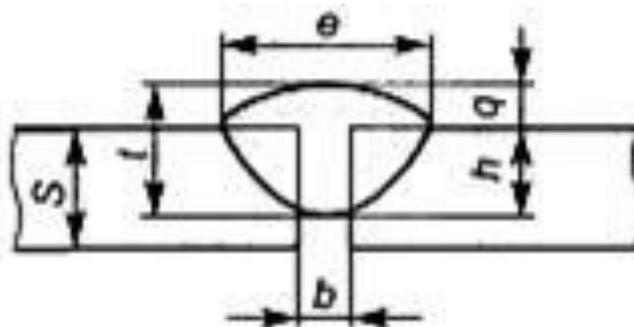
Основные геометрические параметры шва: S – толщина свариваемого металла; e – ширина сварного шва; q – выпуклость стыкового шва (высота усиления) – наибольшая высота (глубина) между поверхностью сварного шва и уровнем расположения поверхности сваренных деталей; h – глубина провара (глубина проплавления) – наибольшая глубина расплавления основного металла;  $t = q + h$ ; b – зазор.
